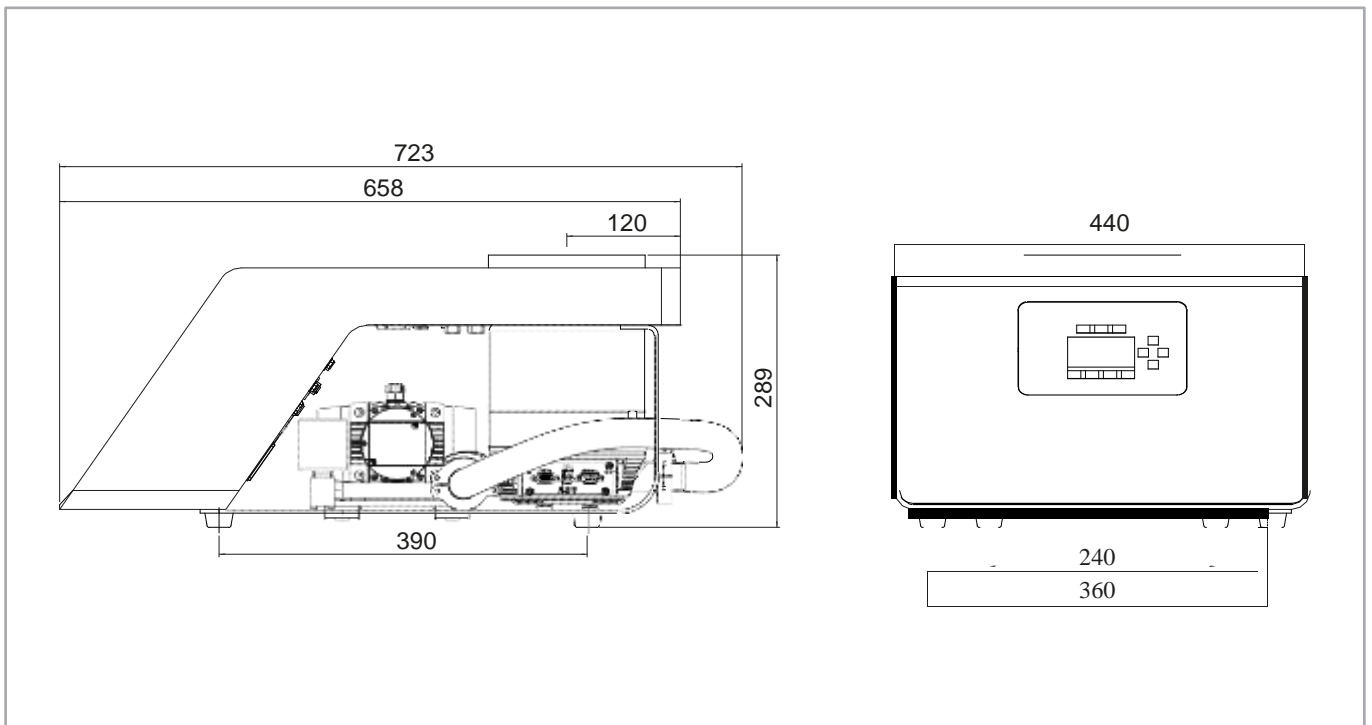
Габаритные размеры TURBOLAB 350/450, размеры в мм
